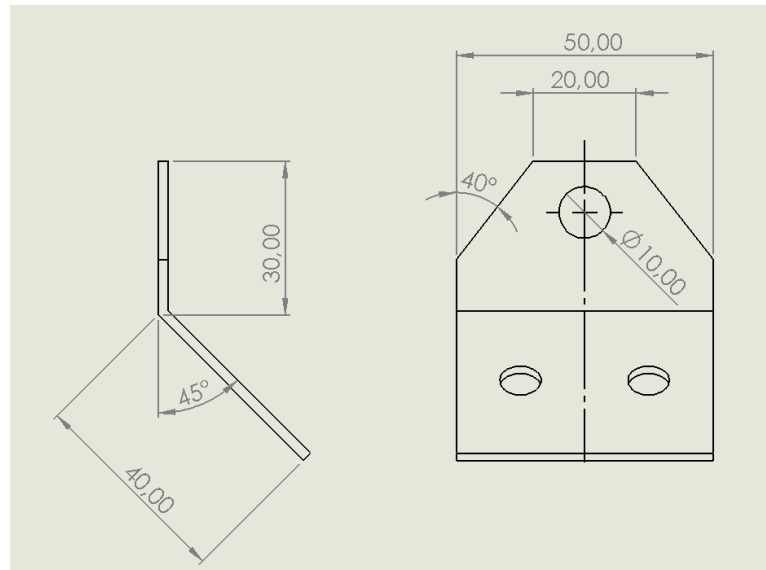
Dimensioni della staffa di fissaggio alla ruota
